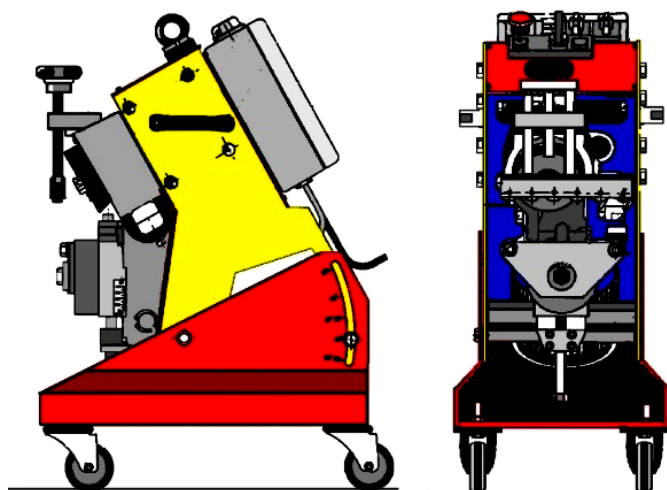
Машина для обработки продольной кромки листа перед сваркой «G. B.C. Industrial Tools» CH 15
